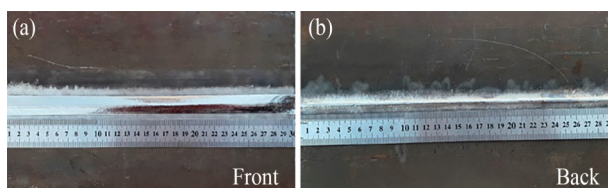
焊缝宏观形貌:(a)焊缝正面;(b)焊缝背面^[21]
